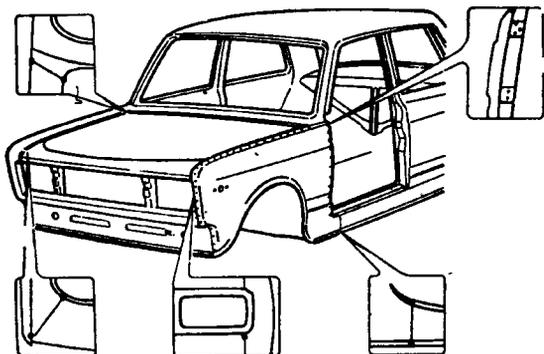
Места сварки переднего крыла. На основном виде точками обозначены швы контактной сварки. На фрагментах показаны точки газовой сварки
